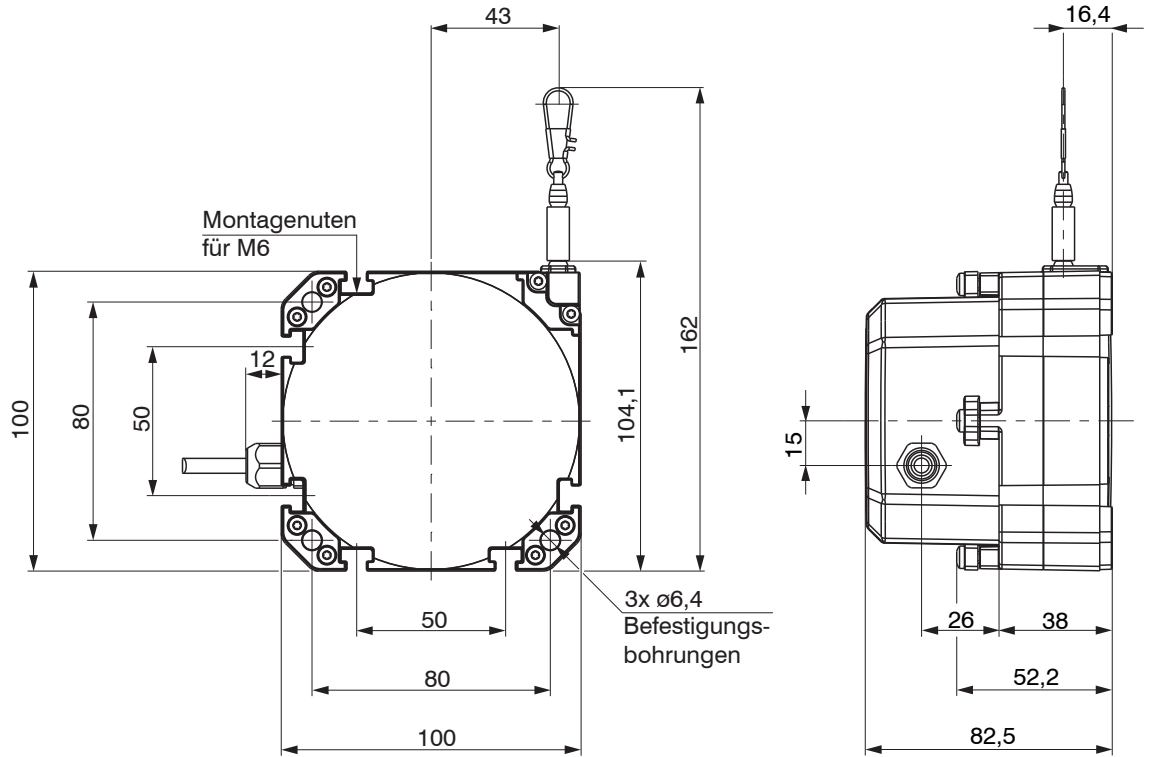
Maßzeichnung WPS-1500-K100, WPS-2500-K100 Abmessungen in mm, nicht maßstabgetreu
